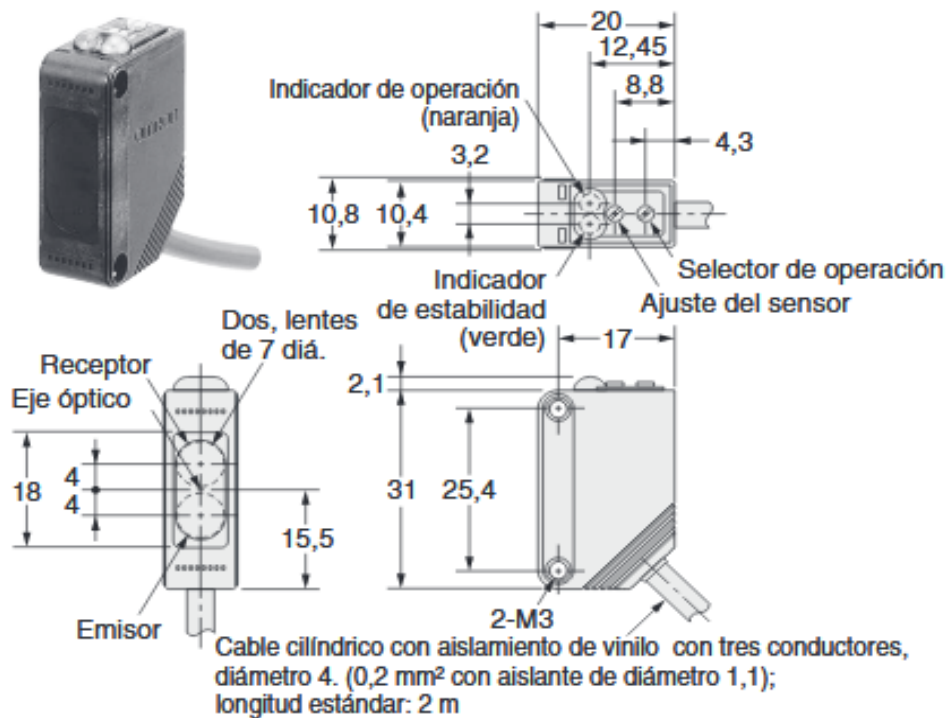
Dimensiones técnicas del sensor E3Z-d62 OMRON
